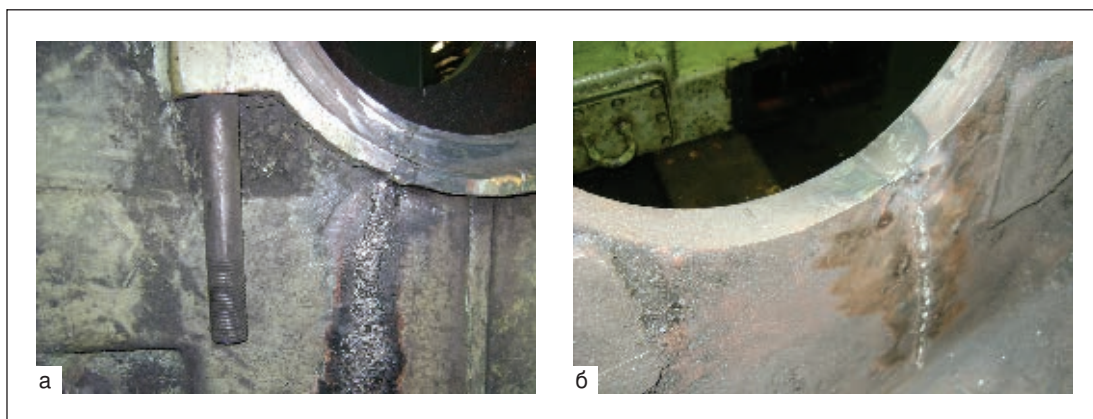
Заваренная трещина в посадочном месте подшипника корпуса редуктора: а — вид снаружи; б — вид изнутри
